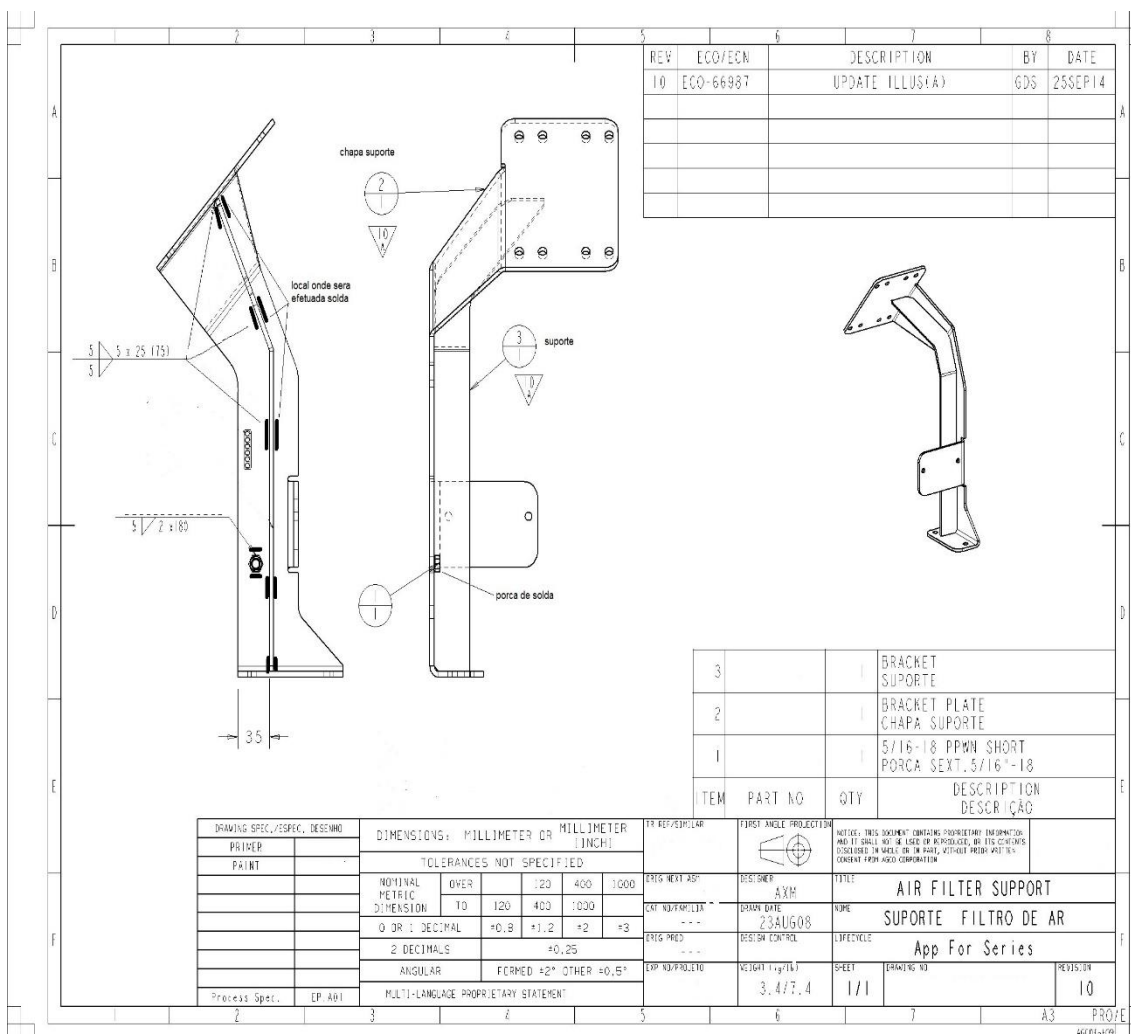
Desenho técnico do componente a ser soldado. Fonte: Adaptado pelo autor
